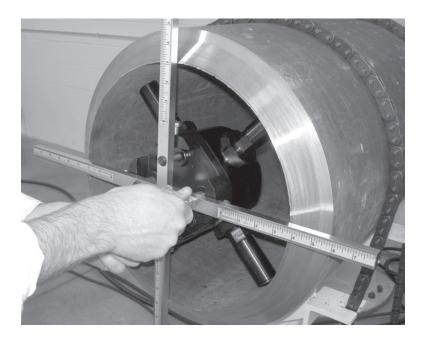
Установите центровочный указатель на шпильки зажимного кулачка.
